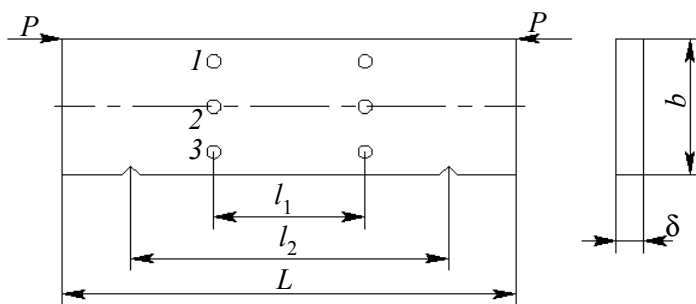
Розташування баз вимірів на штабі для дослідження поздовжньої усадки
